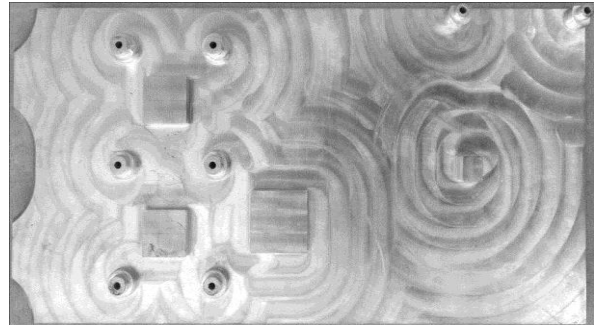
Photo de la plaque de la plaque froide (vue de dessous)
